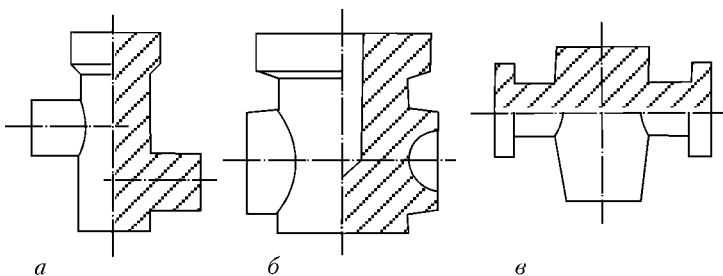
Заготовки корпусов арматуры, работающих при высоком давлении, с различным типом присоединения к трубопроводам: а — вентиль из стали 15X1M1F; б — задвижка из стали 0X18H10T; в — фланцевая задвижка из стали 38XM
